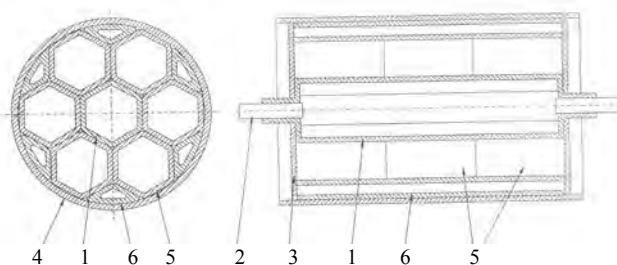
Барабан ленточного конвейера сотовой конструкции
